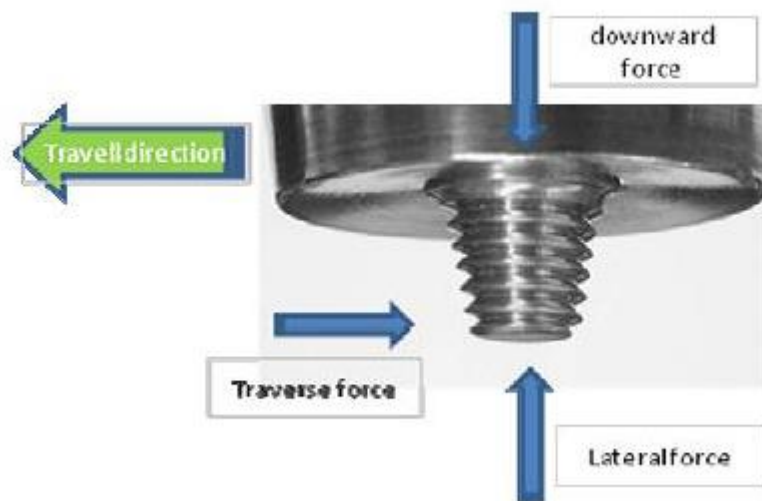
Skema *stir welding* (Polmear, 1995)
